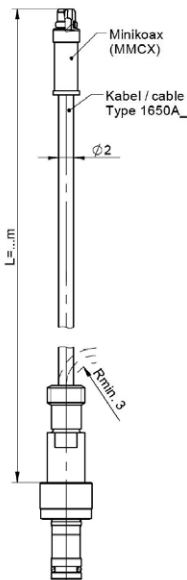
Drucksensor Typ 6177B mit Koaxial Kabel und Mini-Koax Stecker
